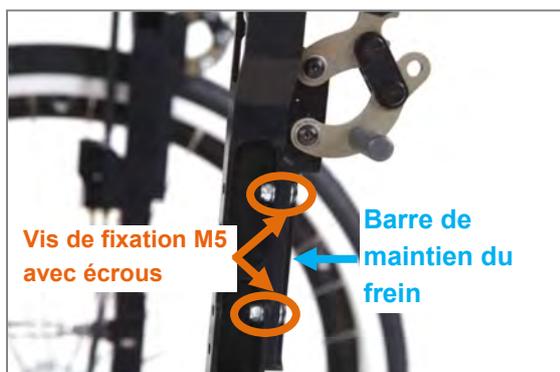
Frein à pousser monté à l'arrière (vue latérale)
